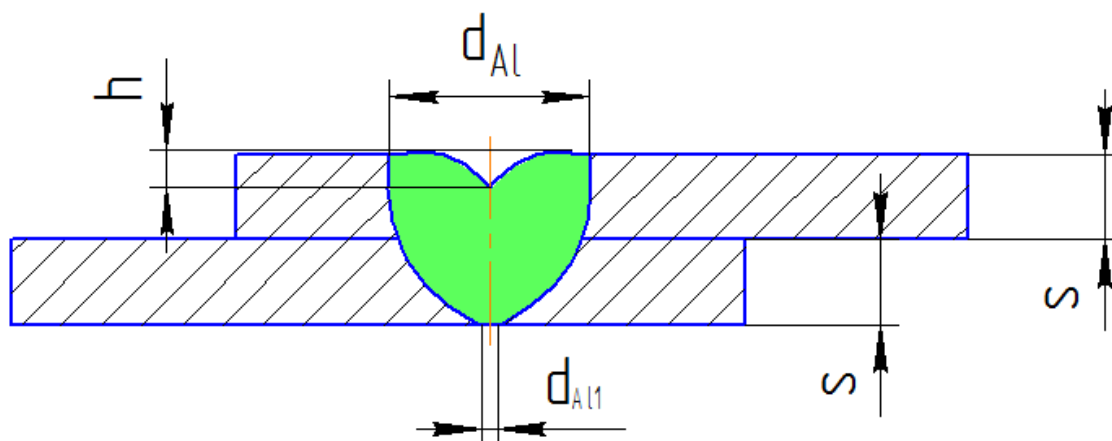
Обозначение геометрических параметров сварной точки
